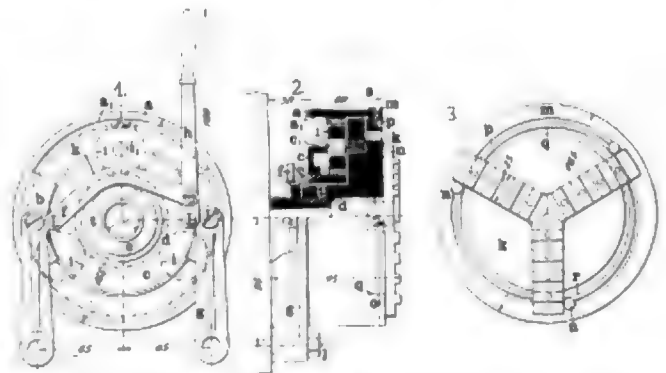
Z. A.: Selbstöffnende Gewindeschneidkluppen und Aufspannfutter für Drehbänke.
